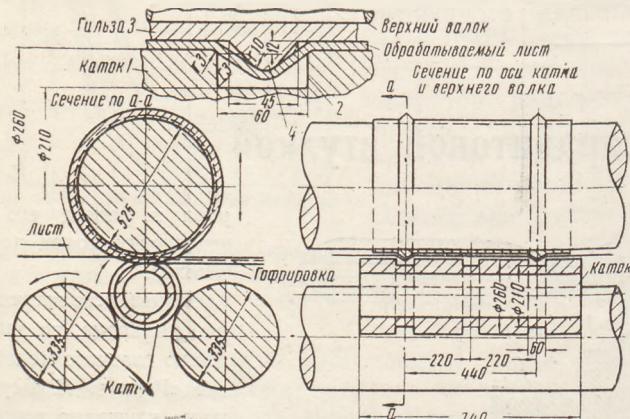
Приспособление для гофрирования листов под гибочными вальцами
